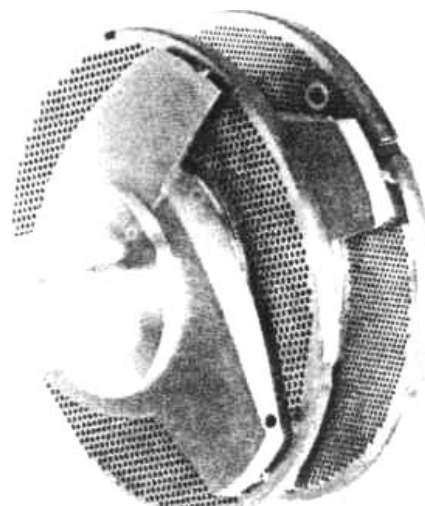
Режущий механизм эмульсатора Karl Schnell
